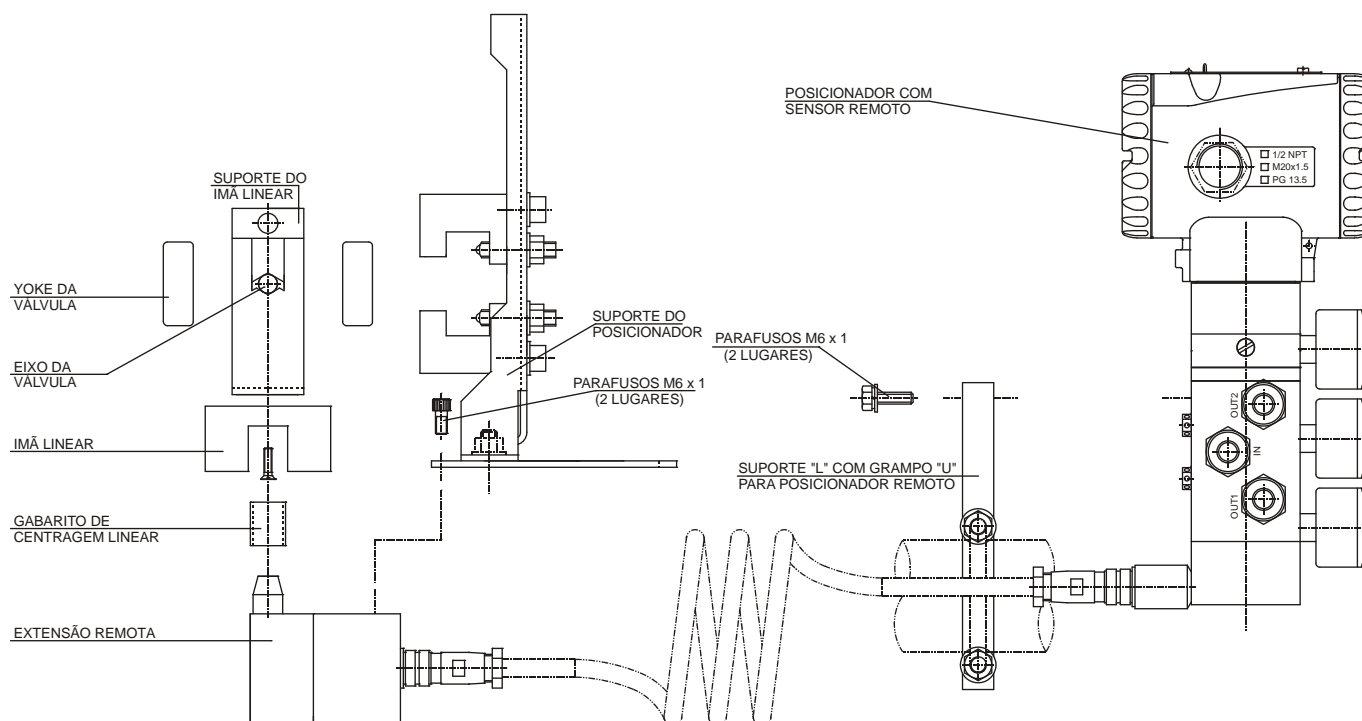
Posicionador em Atuador Linear com Sensor de Posição Remoto
